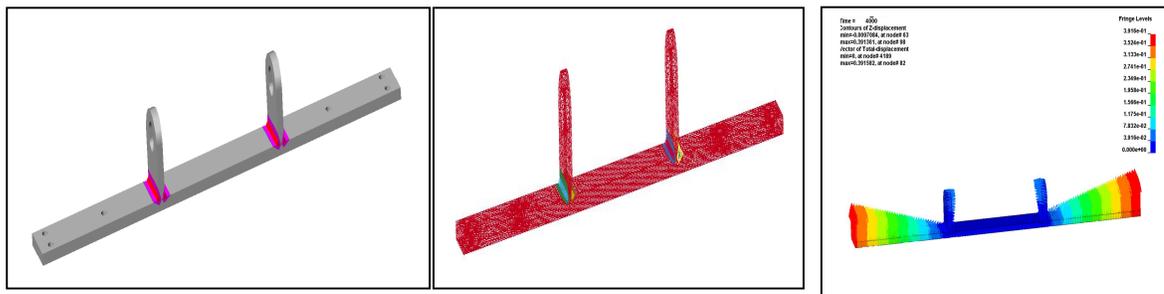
Трёхмерные твердотельные и конечно-элементные модели сварной конструкции
